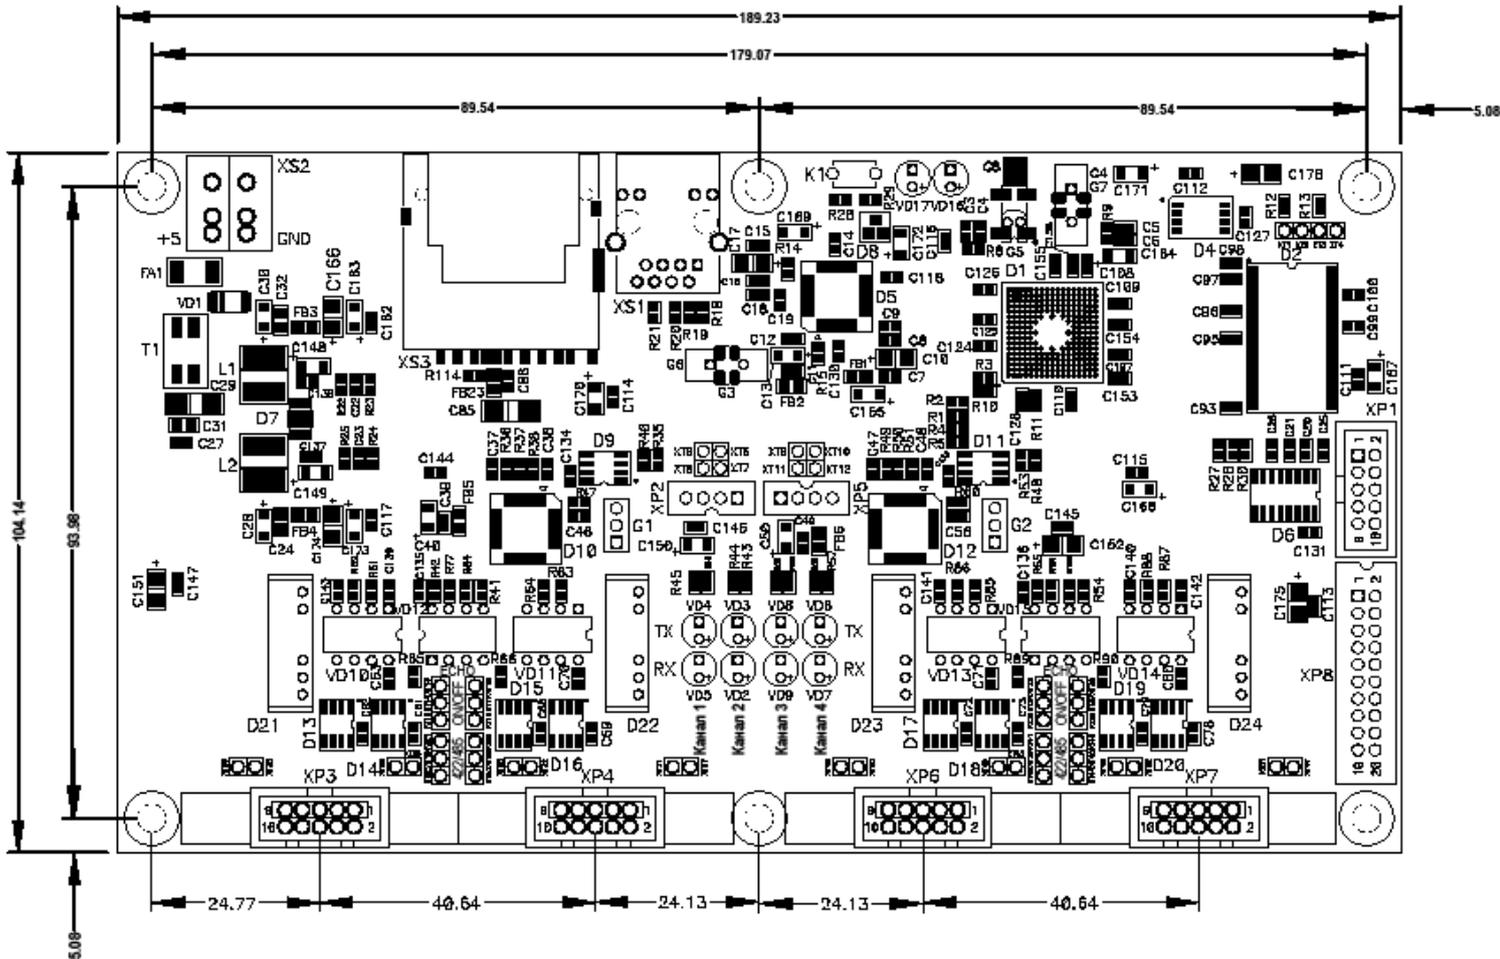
Габаритный чертеж модуля МПИ-4-1.
